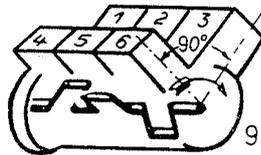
Zylinderbezeichnung beim V-Motor F AL 614
